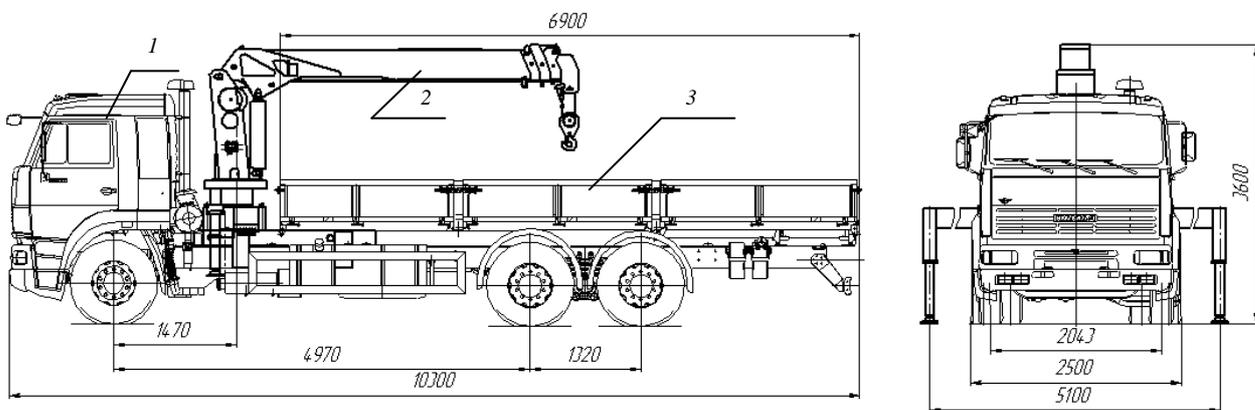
Общий вид 333701 на шасси КАМАЗ-65115-1051-62
